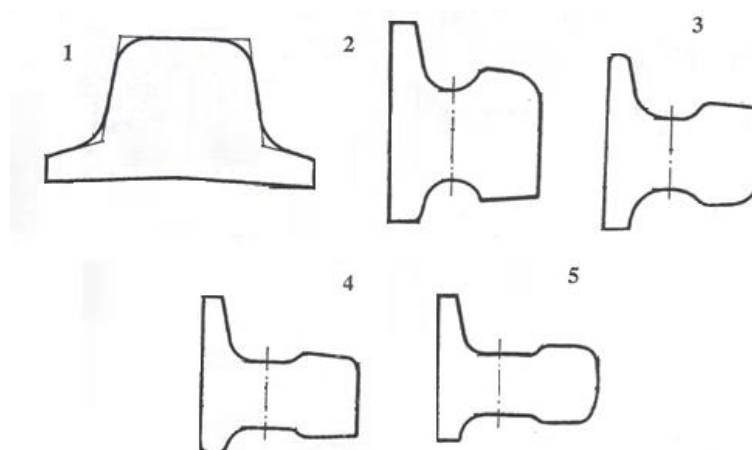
Схема калибровки профиля ОР65 на рельсобалочном стане
